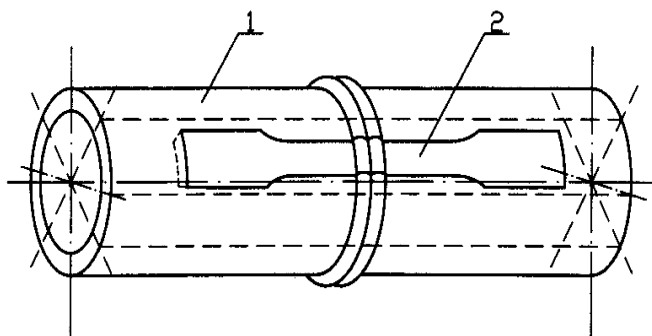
Схема вырезки образцов из сварного соединения для испытания на осевое растяжение:
